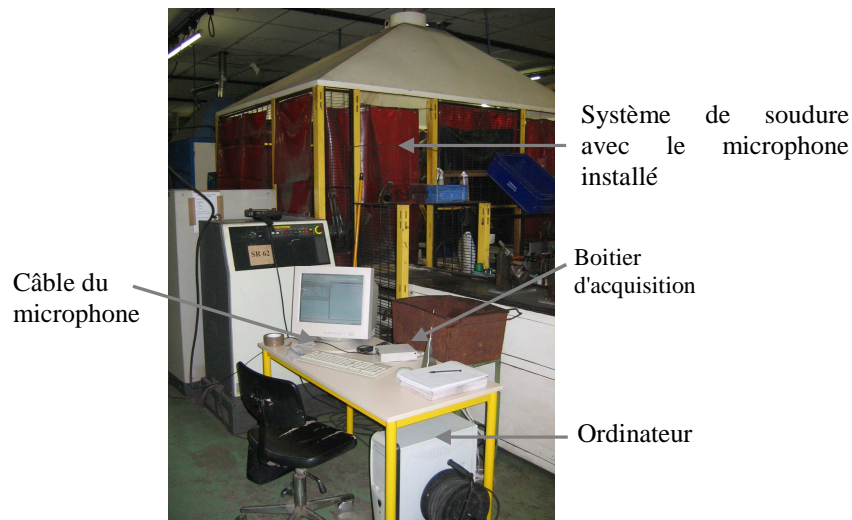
Système d'acquisition installé à proximité de la machine de soudure.
